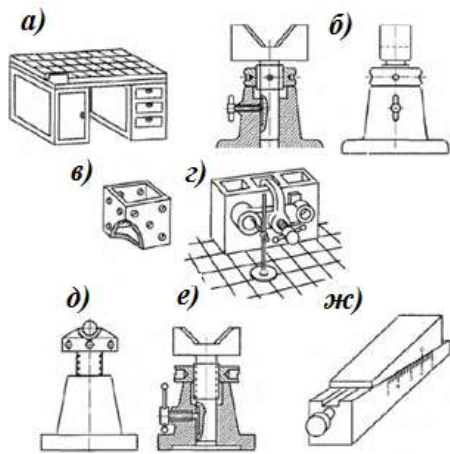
Разметочные устройства: а - стол с чугунной плитой; б - призма с винтовой опорой; в - разметочный ящик - общий вид; г - пример использования; д - домкрат с шаровой и е - призматической опорой для заготовки; ж - разметочный клин
